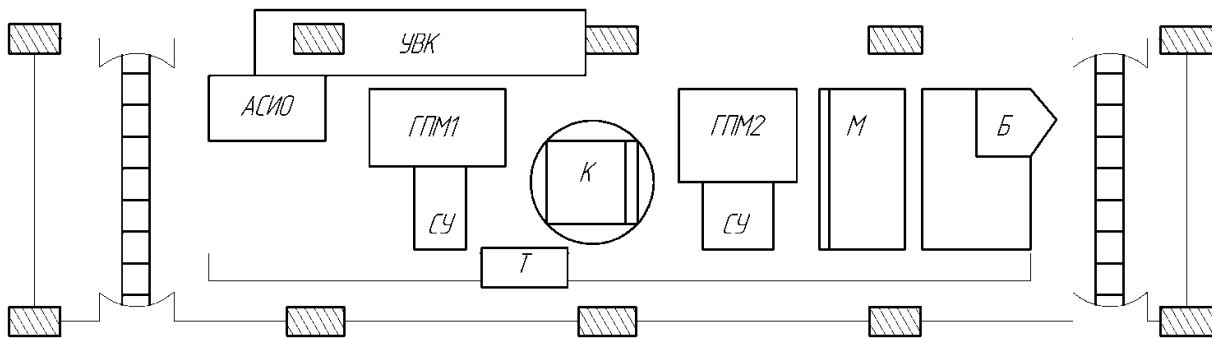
План ГАД з важкими свердильно-фрезерно-розточувальними ОЦ
